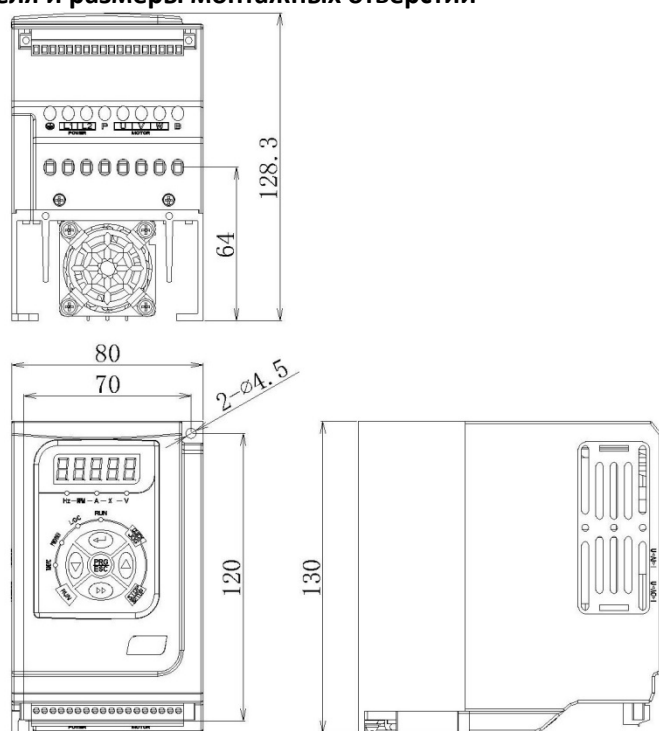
Габариты преобразователя и размеры монтажных отверстий
